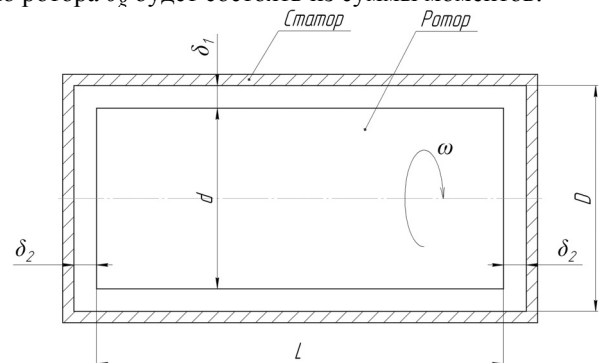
Расчетная схема для определения гидродинамических моментов:
